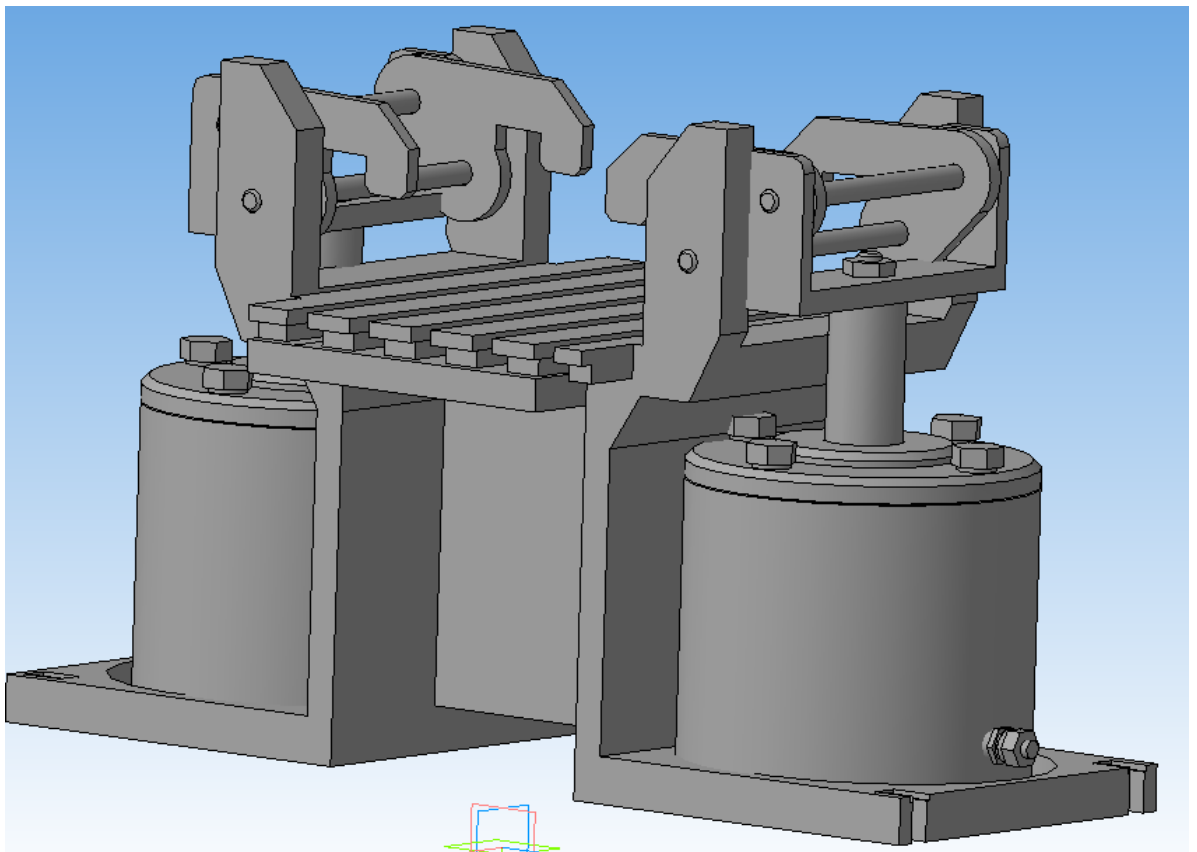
3D модель пристрою для фрезерної обробки кронштейну
